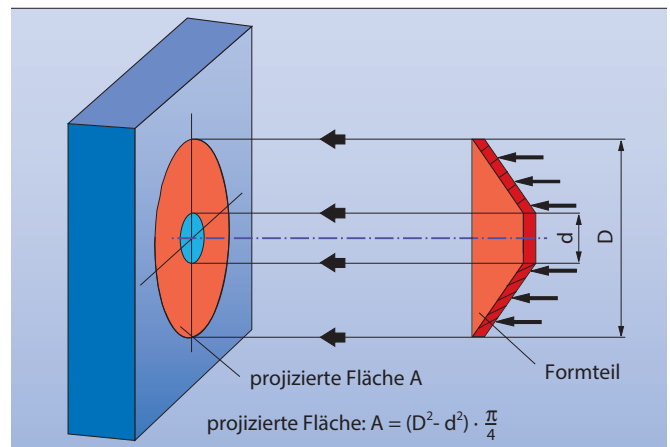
Kegelstumpfförmige Scheibe als Beispiel für die in die Trennebene projizierte, Werkzeugauftrieb erzeugende Fläche
